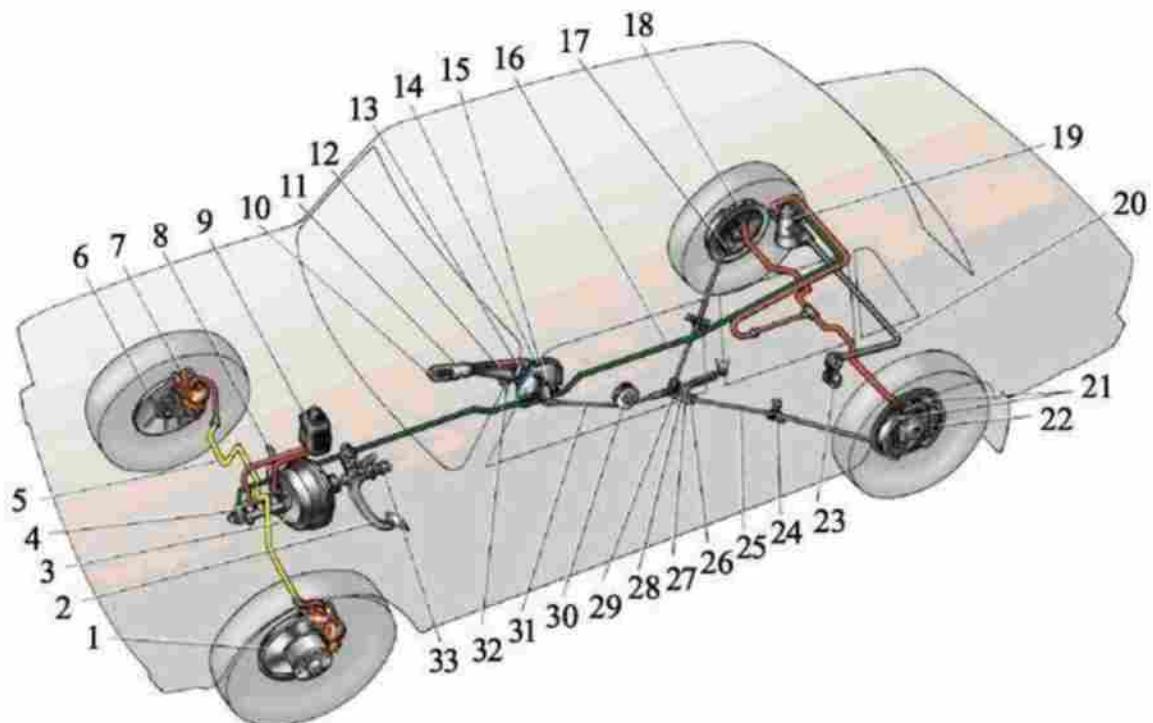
Общая схема тормозной системы: 1 - передний тормоз; 2 - педаль тормоза; 3 - вакуумный усилитель; 4 - главный цилиндр гидропривода тормозов; 5 - трубопровод контура привода передних тормозов; 6 - защитный кожух переднего тормоза; 7 - суппорт переднего тормоза; 8 - вакуумный трубопровод; 9 - бачок главного цилиндра; 10 - кнопка рычага привода стояночного тормоза; 11 - рычаг привода стояночного тормоза; 12 - тяга фиксатора рычага; 13 - фиксатор рычага; 14 - кронштейн рычага привода стояночного тормоза; 15 - возвратный рычаг; 16 - трубопровод контура привода задних тормозов; 17 - фланец наконечника оболочки троса; 18 - задний тормоз; 19 - регулятор давления задних тормозов; 20 - рычаг привода регулятора давления; 21 - колодки заднего тормоза; 22 - рычаг ручного привода колодок; 23 - тяга рычага привода регулятора давления; 24 - кронштейн крепления наконечника оболочки троса; 25 - задний трос; 26 - контргайка; 27 - регулировочная гайка; 28 - втулка; 29 - направляющая заднего троса; 30 - направляющий ролик; 31 - передний трос; 32 - упор выключателя контрольной лампы стояночного тормоза; 33 - выключатель стоп-сигнала.
